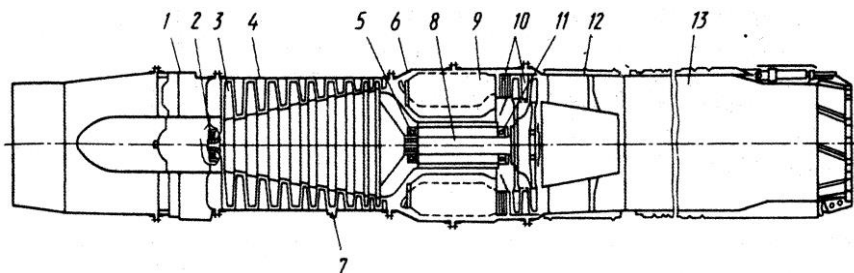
Одновальный турбореактивный двигатель с форсажной камерой: 1, 4, 6 - передний, средний и задний корпуса компрессора; 2, 5, 11 - передняя, средняя и задняя опоры ротора двигателя; 3 - ротор компрессора; 7 - механизм перепуска; 8 - ротор газовой турбины; 9 - камера сгорания; 10 - сопловые аппараты газовой турбины; 12 - диффузор форсажной камеры; 13 - регулируемое реактивное сопло
